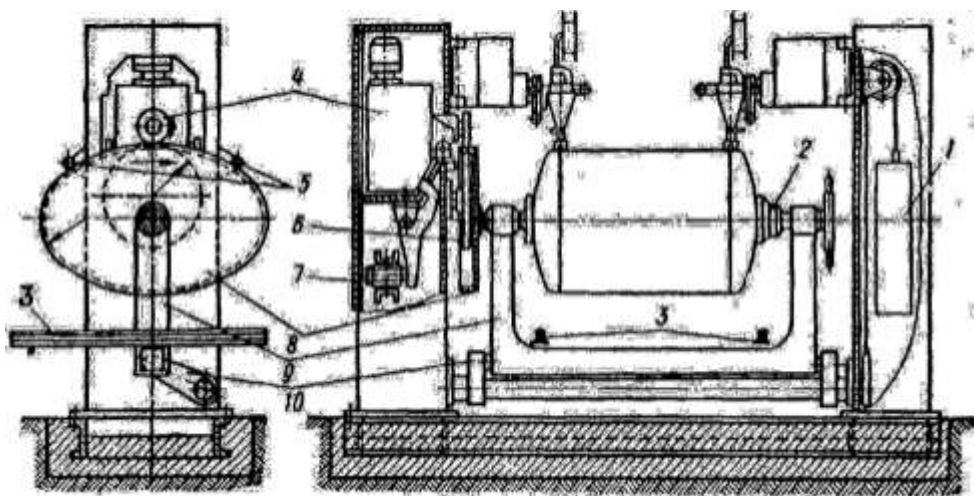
Схема установки для автоматической сварки овальных сосудов
